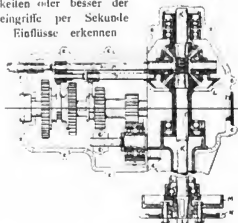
Vertikal- und Horizontalschnitt durch den Getriebekasten des englischen Daimler-Wagen 1905. Bemerkenswert ist das sehr frei liegende Kegelrad, die feste Gehäuseverbindung bis zum Kettenlager s. a. Fig. 9, 10 und die Kettenräder mit angeschraubten Bremsbändern.
